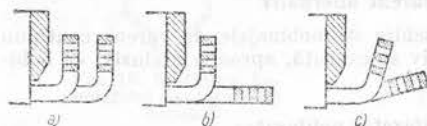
Capetele de bobină la bobinajul în două etaje.
